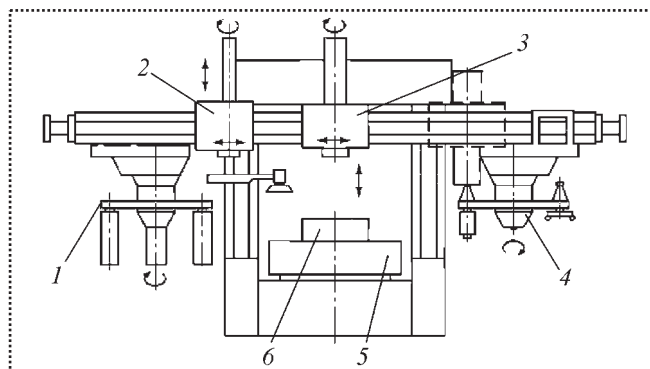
Компоновка сборочного центра с магазинами деталей и инструментов:
